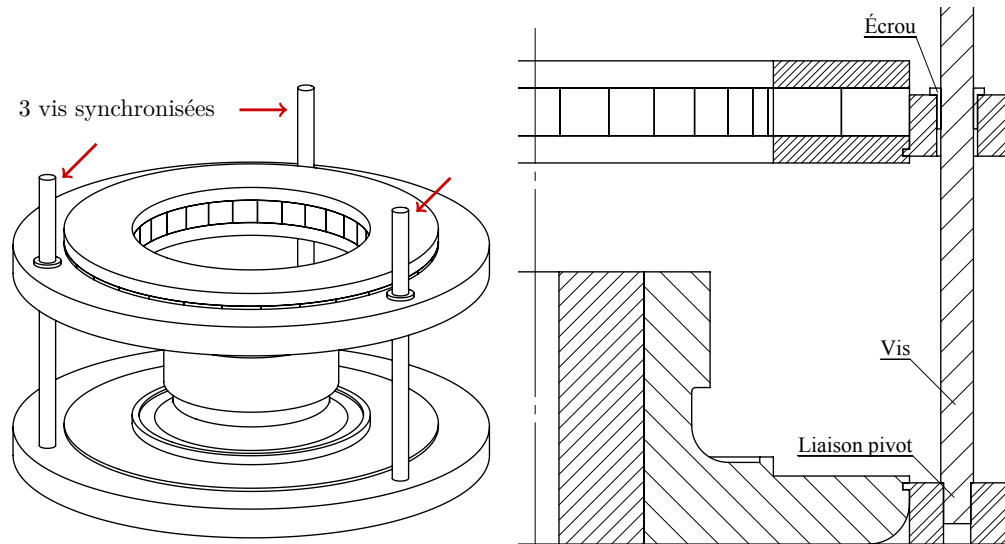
Schéma de principe de la machine d'assemblage de la couronne d'aimants et des pôles. À gauche, vue isométrique ; à droite demi-coupe radiale de l'assemblage. Le mécanisme de synchronisation des trois vis n'est pas représenté.
